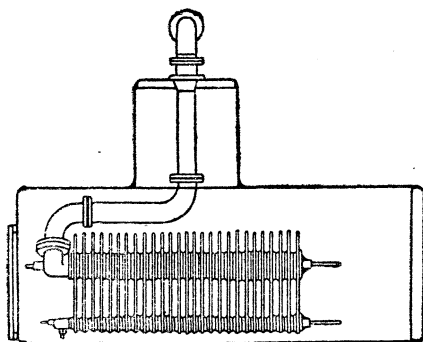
а. Внутренний вид корпуса (элемента) опреснителя сист. Ягна
